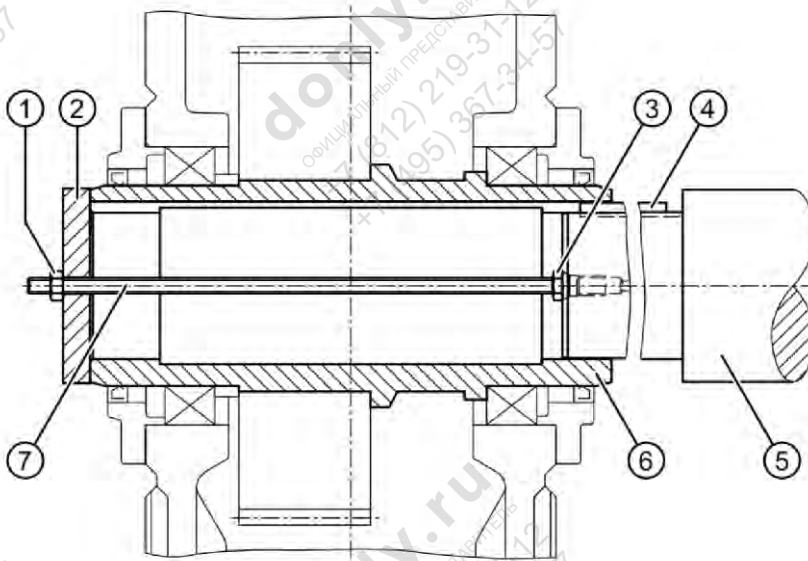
Винтовой шпindel для редукторов с полым валом и шпоночным пазом
